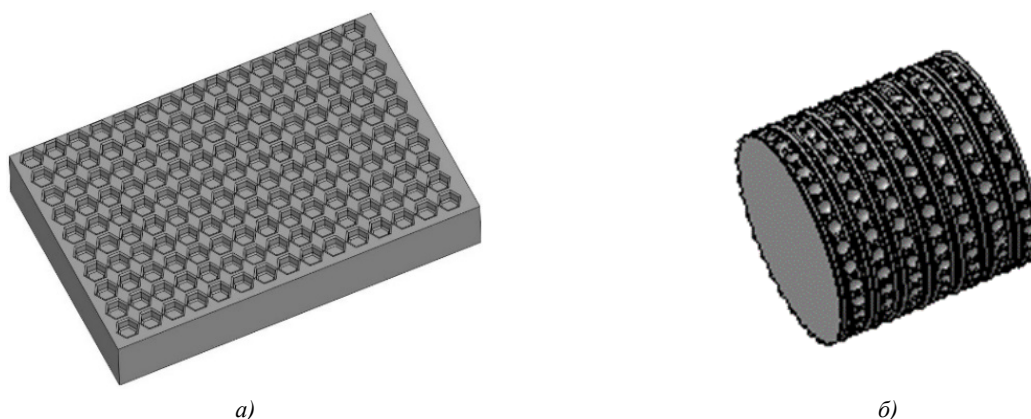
3D-модели ЧРМР: а — на плоской поверхности; б — на цилиндрической поверхности
